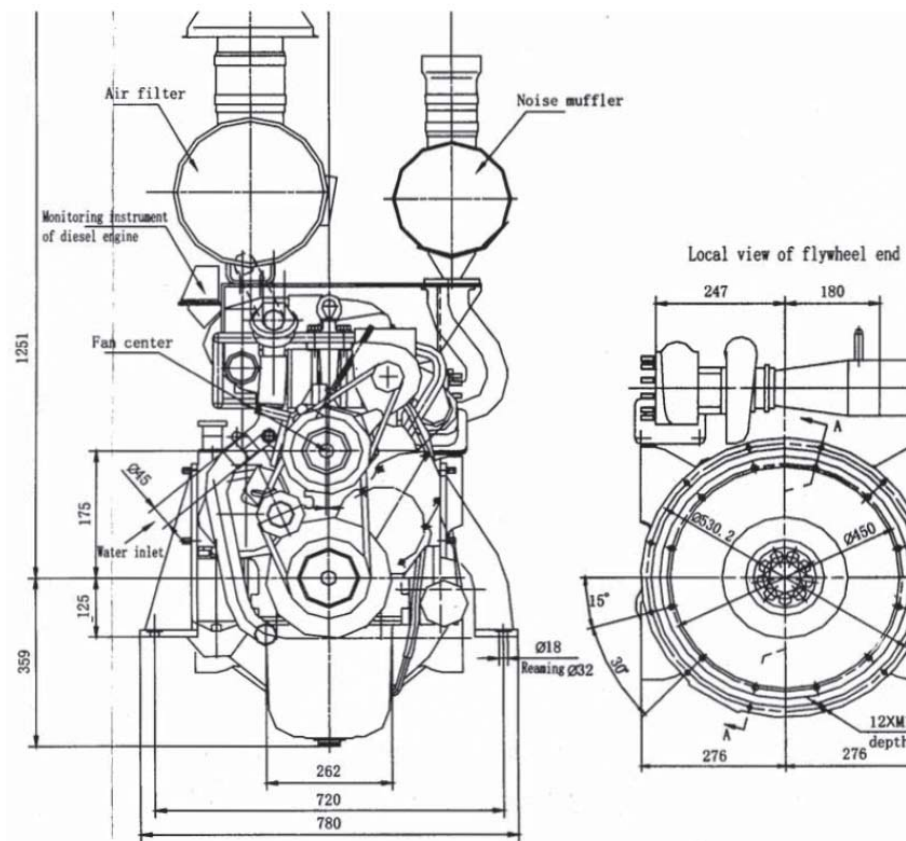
Загальний вид двигуна 6ЧН 12,6/13 (вид спереду)
